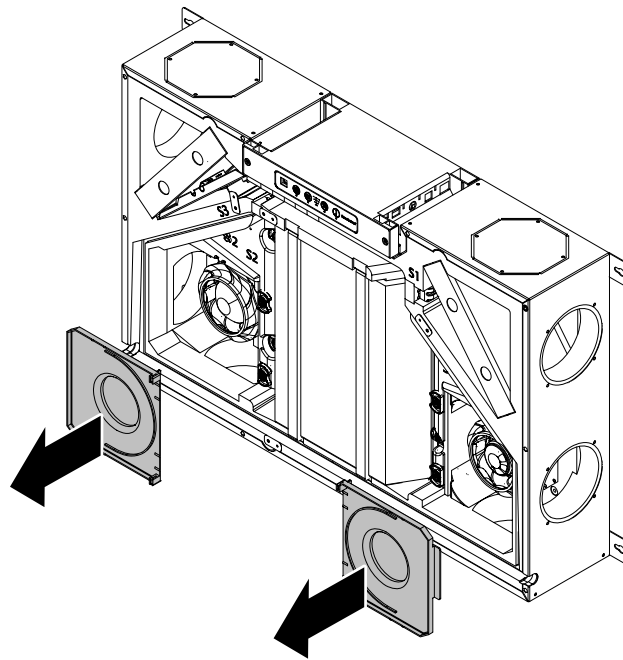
Desmontaje de las cubiertas de los ventiladores
